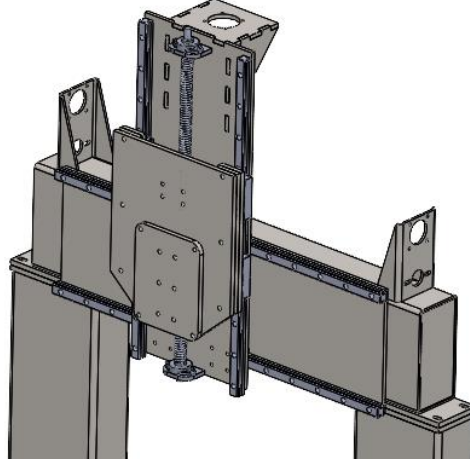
Z motor plakası ve bayraklarının montajı
